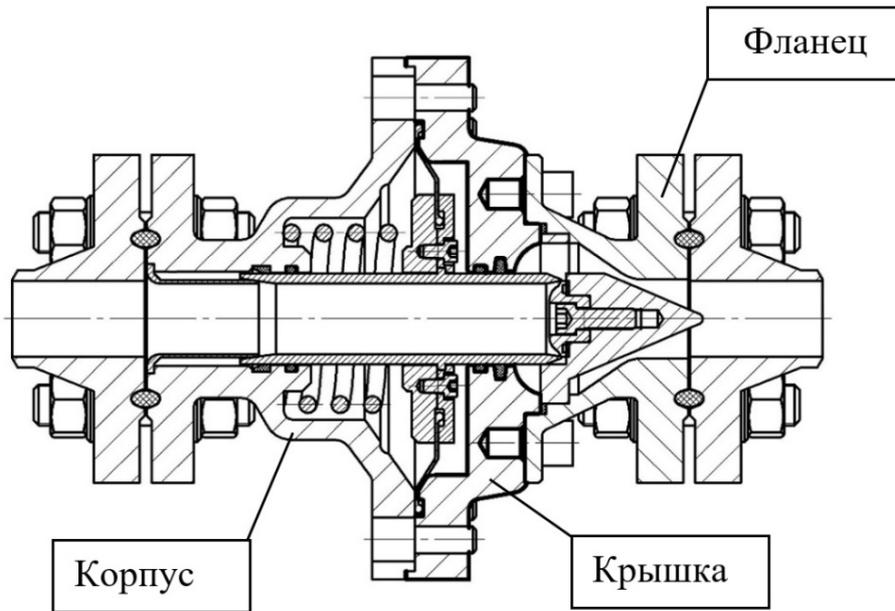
«Крышка» в сборке регулятора РДУ-80-50
